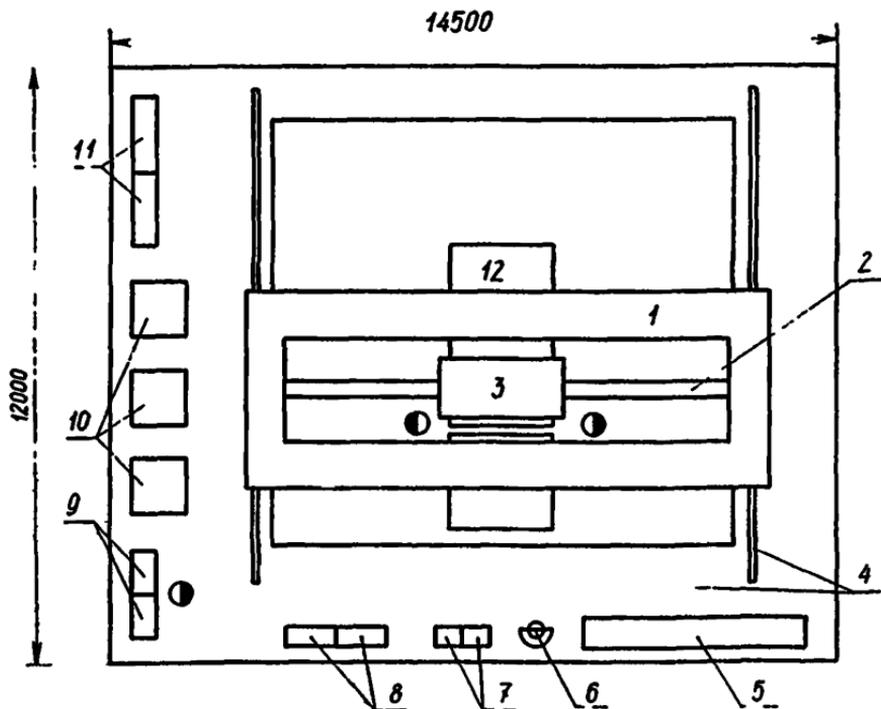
Схема организации рабочего места при электрошлаковой сварке
